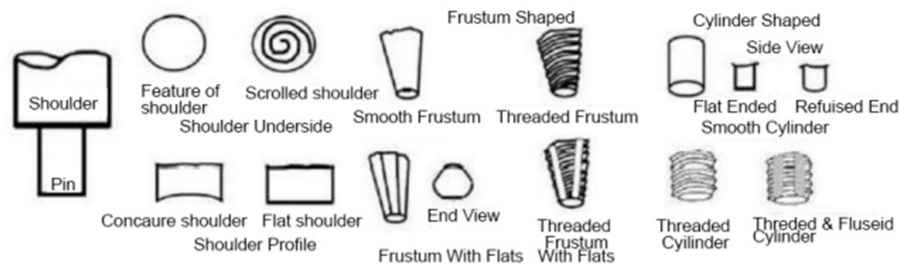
Desain Pin Pada Welding Tool FSW
